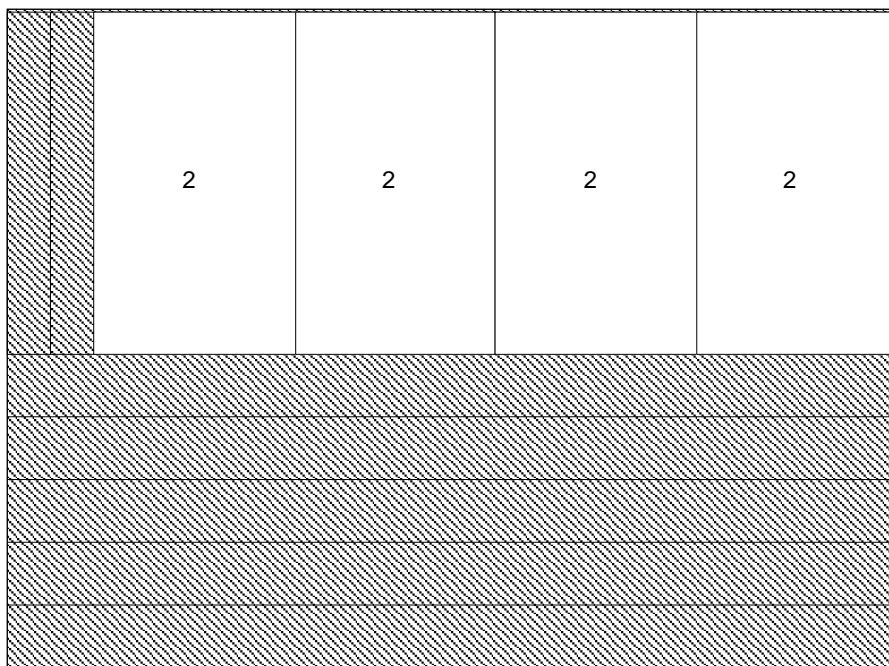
Plano de corte da costa gabinete ilha. Fonte: Dados do autor.
